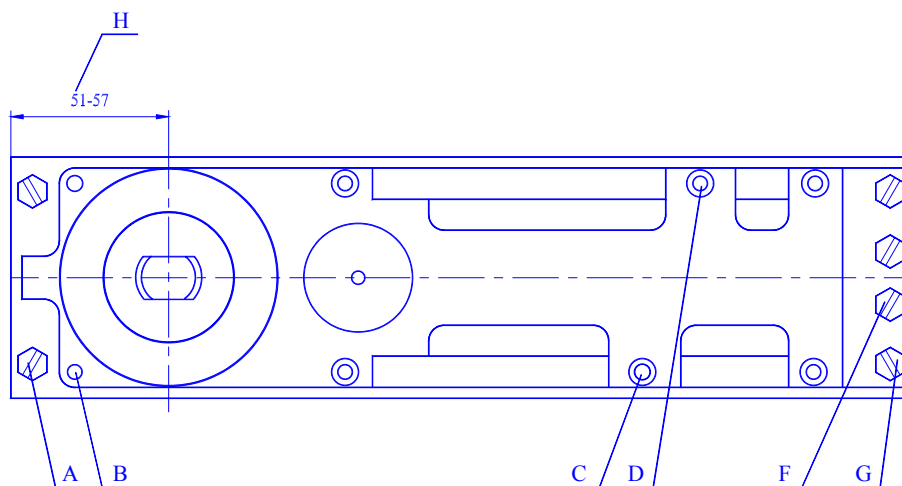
Доводчик-закрыватель напольный BTS-75 (вид со снятой крышкой).
